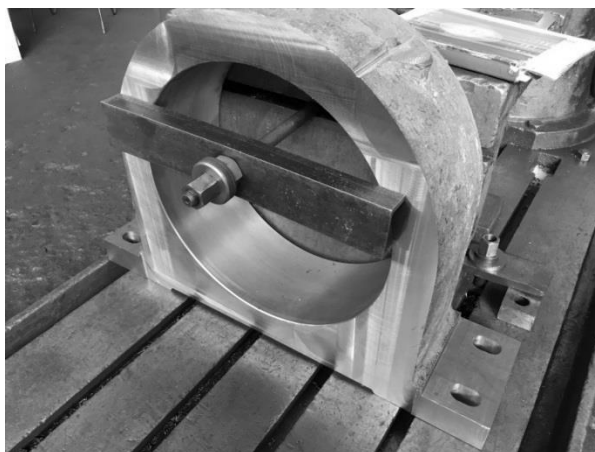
Отливка корпуса подшипника без видимых дефектов
